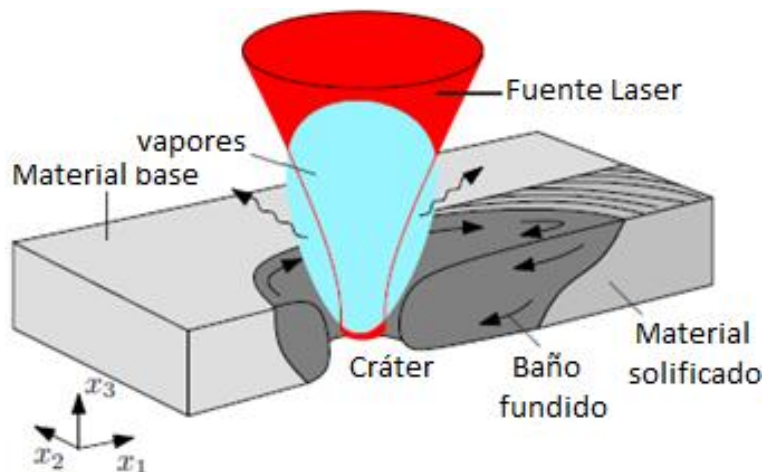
Esquema de soldadura láser en modo de cráter de una lámina delgada.
